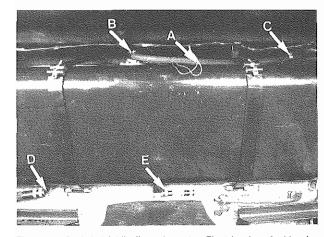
A - Cavi elettrici livello carburante - Electric wires, fuel level
